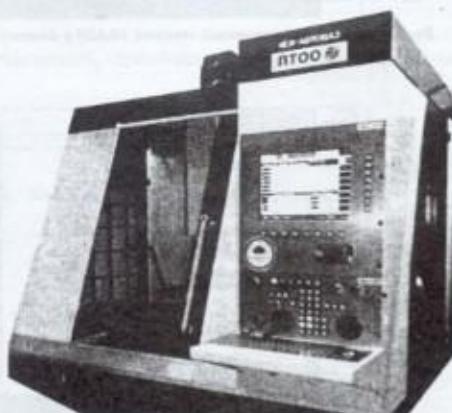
Экспериментальный образец фрезерного обрабатывающего центра МС-400 (ПТОО АвтоВАЗ) с комплексной системой управления (МГТУ "Станкин") (демонстрировался на выставке "Металлообработка-2010")
